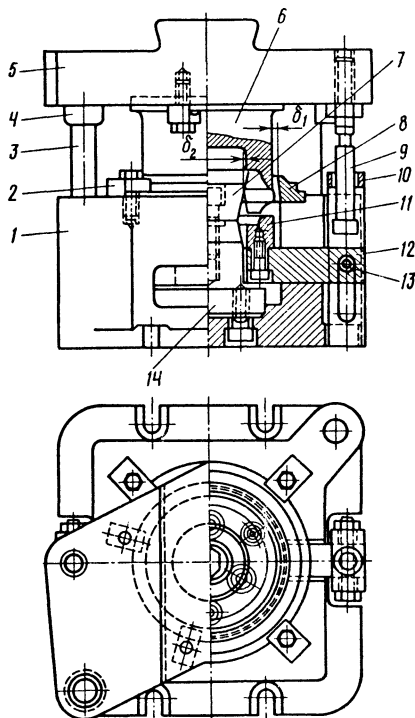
Совмещенный штамп для обрезки и пробивки:
